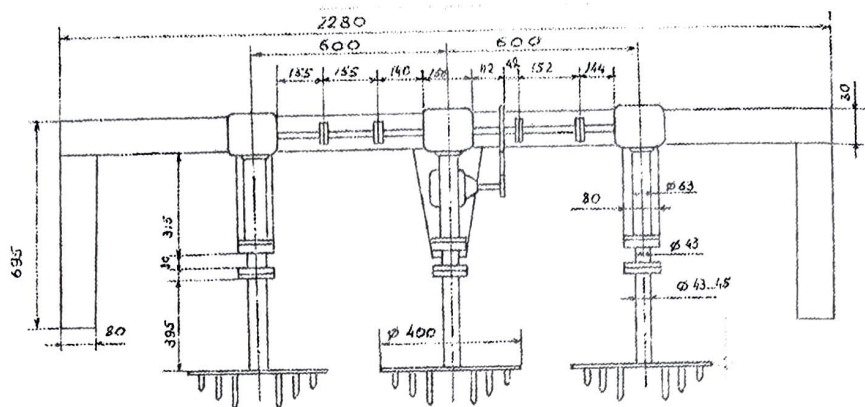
Компоновка на культиватореборонки и привод их вращения.
